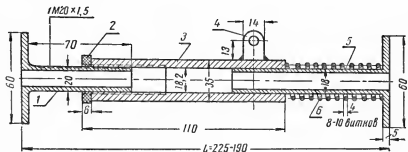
Приспособление для замера расхождения щек коленчатого вала:
